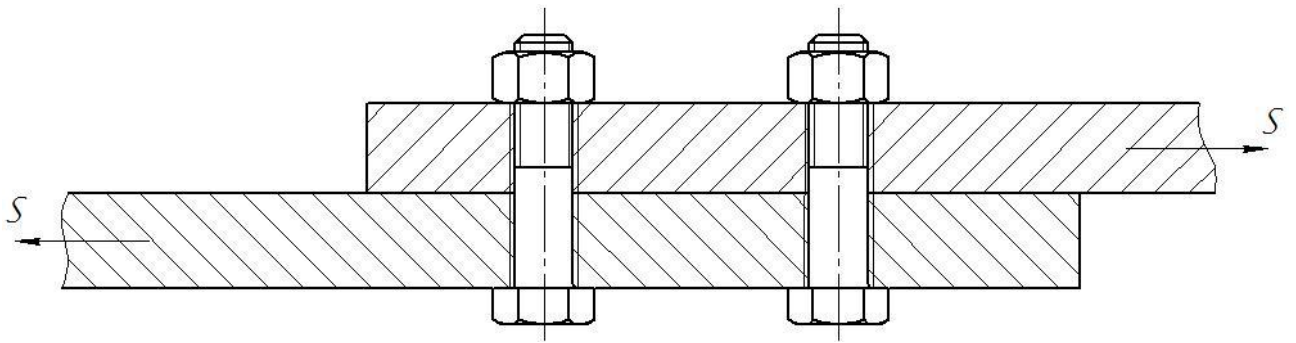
Розрахункова схема різьбового з'єднання з встановленням чистих болтів
